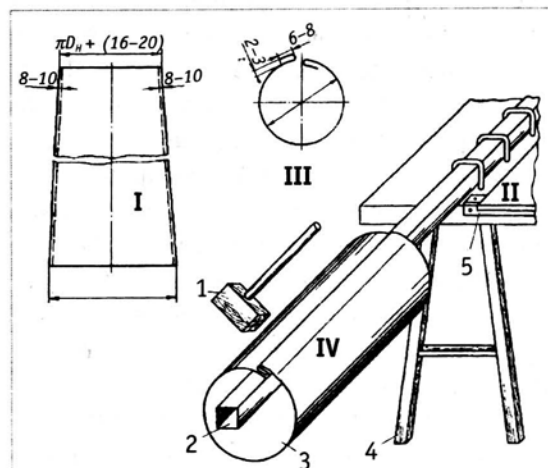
Изготовление отдельной трубы: I — заготовка; II — загиб кромок; III — свертывание цилиндра; IV — соединение кромок в одинарный лежащий фальц; 1 — киянка (деревянный молоток); 2 — брус-оправка; 3 — труба; 4 — верстак; 5 — уголок
